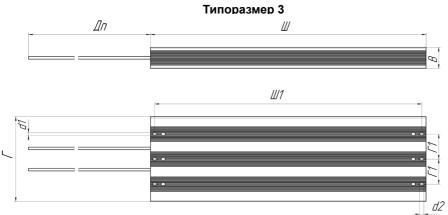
Габаритно-установочные чертежи резисторов серии IBRA
